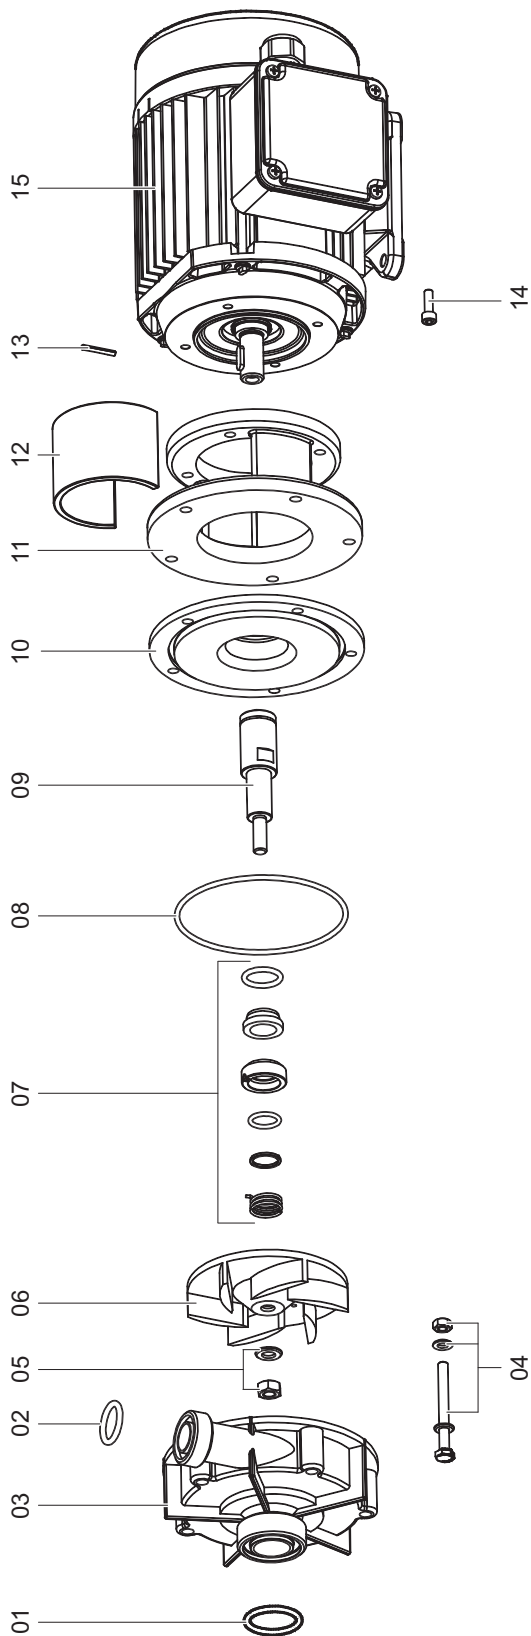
Teile (Explosionszeichnung), Beispiel Baureihe U
